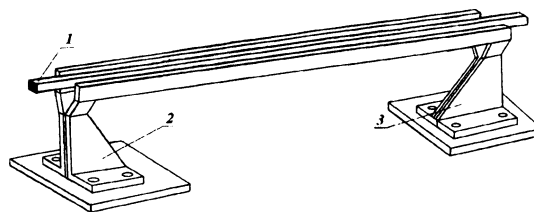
Индуктор для нагрева заготовок чизельного зуба под навивку: 1 — заготовка; 2, 3 — токоподводящие шины индуктора
